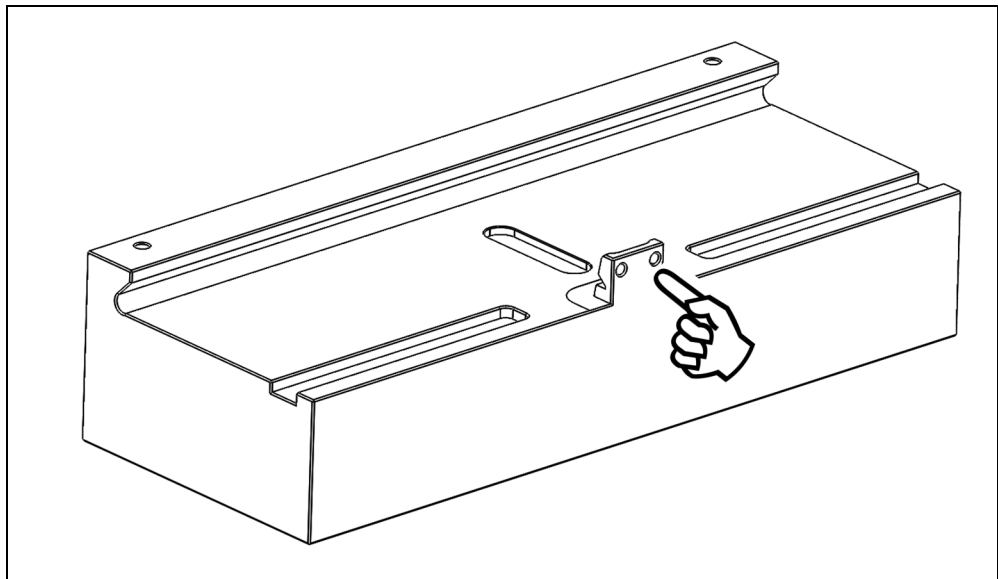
Hinweis auf die Gewinde für die Sicherheitsschrauben
